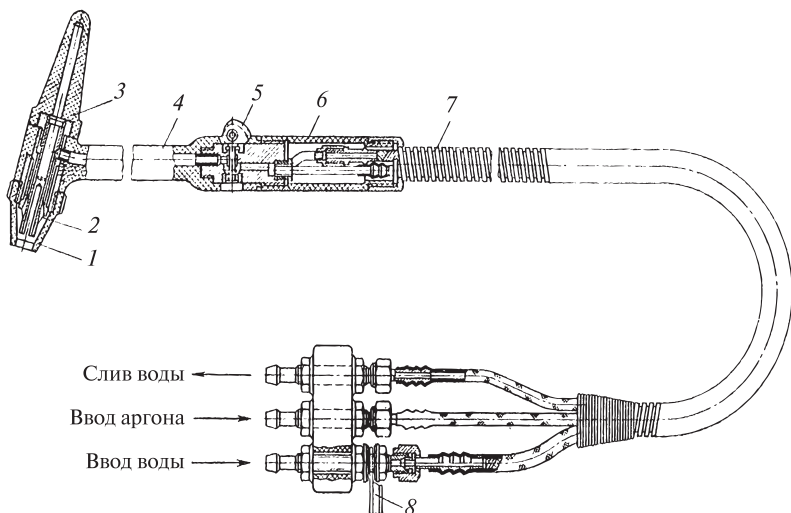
Горелка для ручной сварки вольфрамовым электродом:
